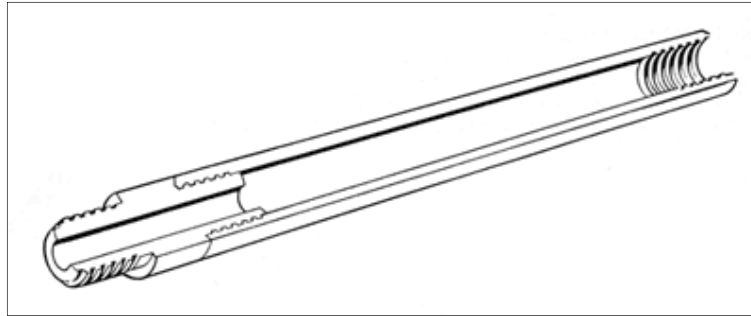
Corte longitudinal em uma haste de perfuração.
